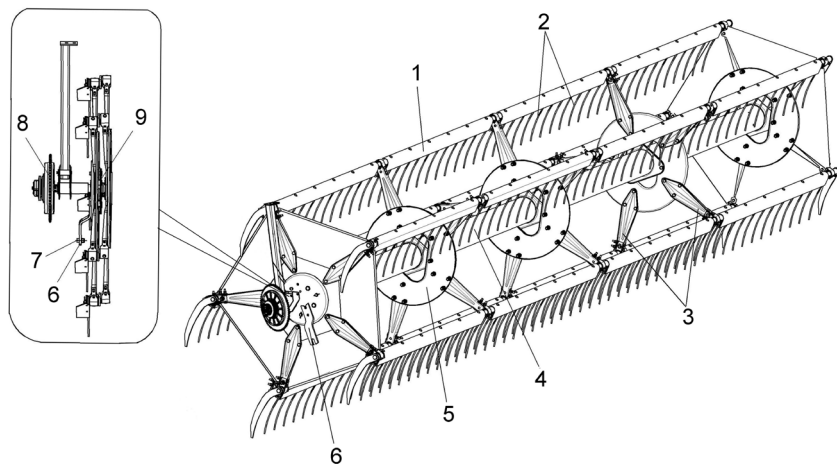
Мотовило: 1 – граблина; 2 – пружинные пальцы; 3 – луч; 4 – вал мотовила; 5 – диск; 6 – поводок; 7 – ролик; 8 – приводная звездочка с предохранительной муфтой; 9 – эксцентриковый механизм
